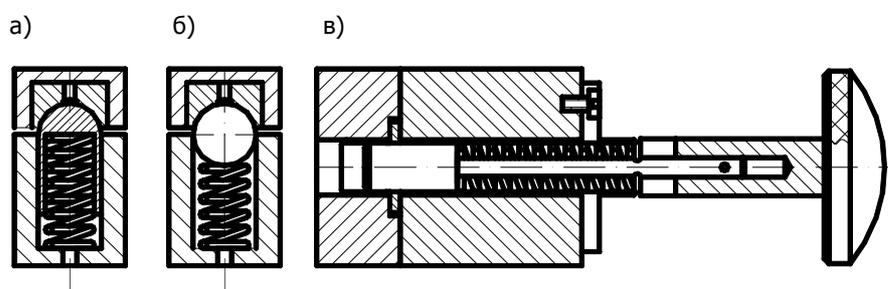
Примеры конструкции фиксаторов, применяемых в делительных устройствах: а – с погруженным пустотелым пальцем; б – с погруженным шариком; в – с вытяжным цилиндрическим пальцем: 1 – втулка; 2 – штифт; 3 – вытяжная кнопка; 4 – цилиндрический фиксатор.
